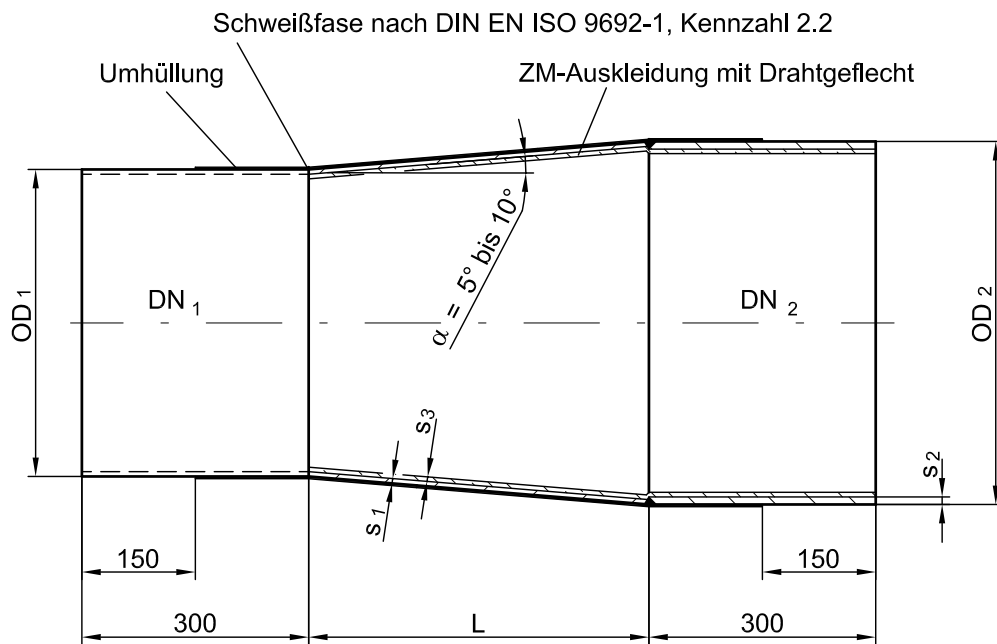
Reduzierungen von Stahl- auf Gussrohr (R-Stücke) – Ausführung H
